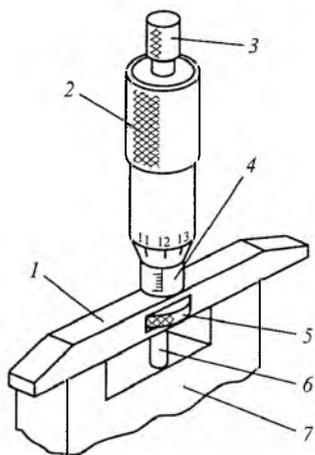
Микрометрический глубиномер: 1 – поперечина; 2 – барабан; 3 – трещотка; 4 – стембель; 5 – стопорный винт; 6 – сменный стержень; 7 – проверяемая деталь
